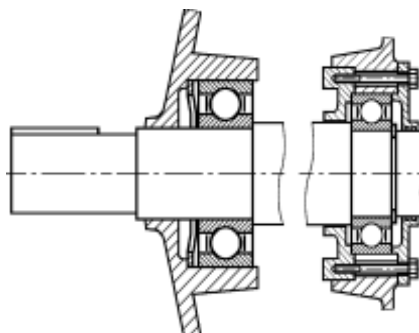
для двигателей габаритов 160, 180 мм
